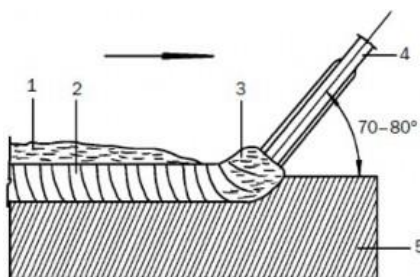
Положение электрода при сварке с глубоким проплавлением (стрелкой указано направление сварки): 1 – шлак; 2 – металл шва; 3 – сварной шов; 4 – электрод; 5 – основной металл
